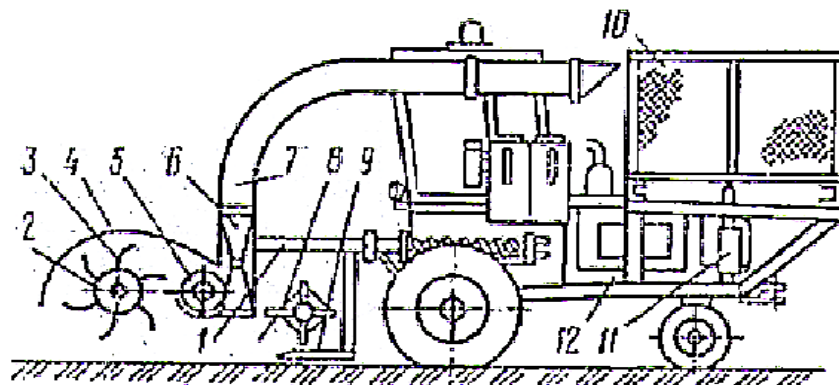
Схематический разрез навесной кормоуборочной установки
